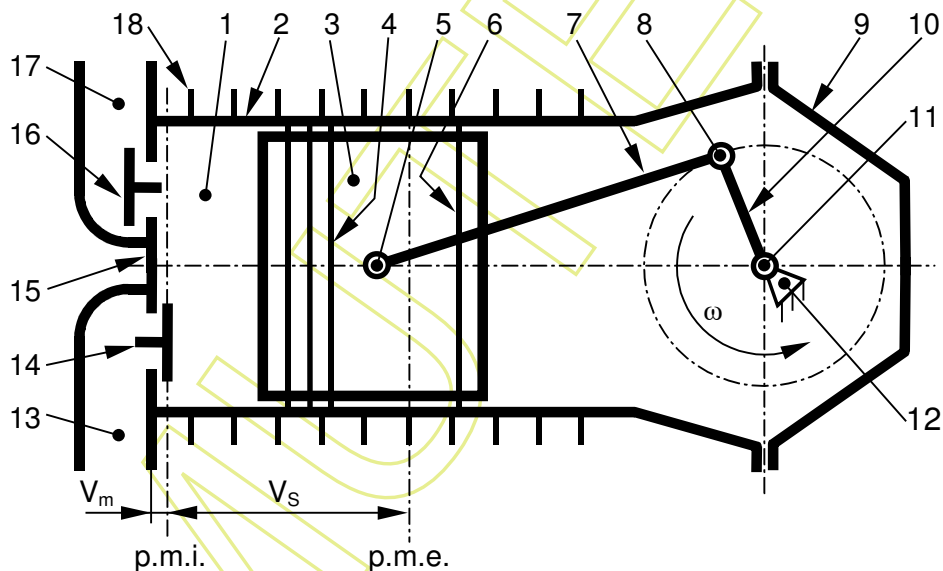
Schema de principiu a unui compresor cu piston cu mișcare de translație: 1 - spațiul de lucru; 2 - cilindru; 3 - piston; 4 - segment de etanșare; 5 - bolt; 6 - segment raclor; 7 - bielă; 8 - fus maneton; 9 - carter; 10 - brațul arborelui cotit; 11 - fus palier; 12 - lagăr de palier; 13 - galerie de aspirație; 14 - supapă de aspirație; 15 - chiulasă; 16 - supapă de refulare; 17 - galerie de refulare; 18 - aripioare de răcire; V_s - cilindree; V_m - volumul mort; p.m.i. - punct mort interior; p.m.e. - punct mort exterior; ω - viteza unghiulară a arborelui cotit
